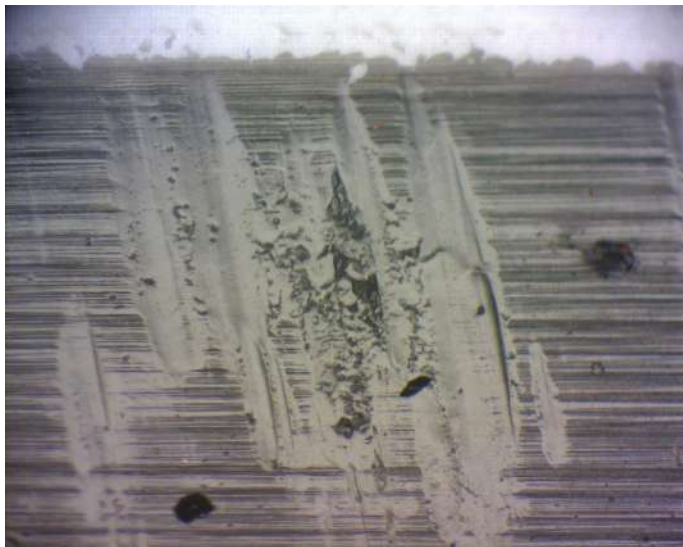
Impressão da superfície antes da aplicação no gearbox da turbina eólica nº 01- 14
